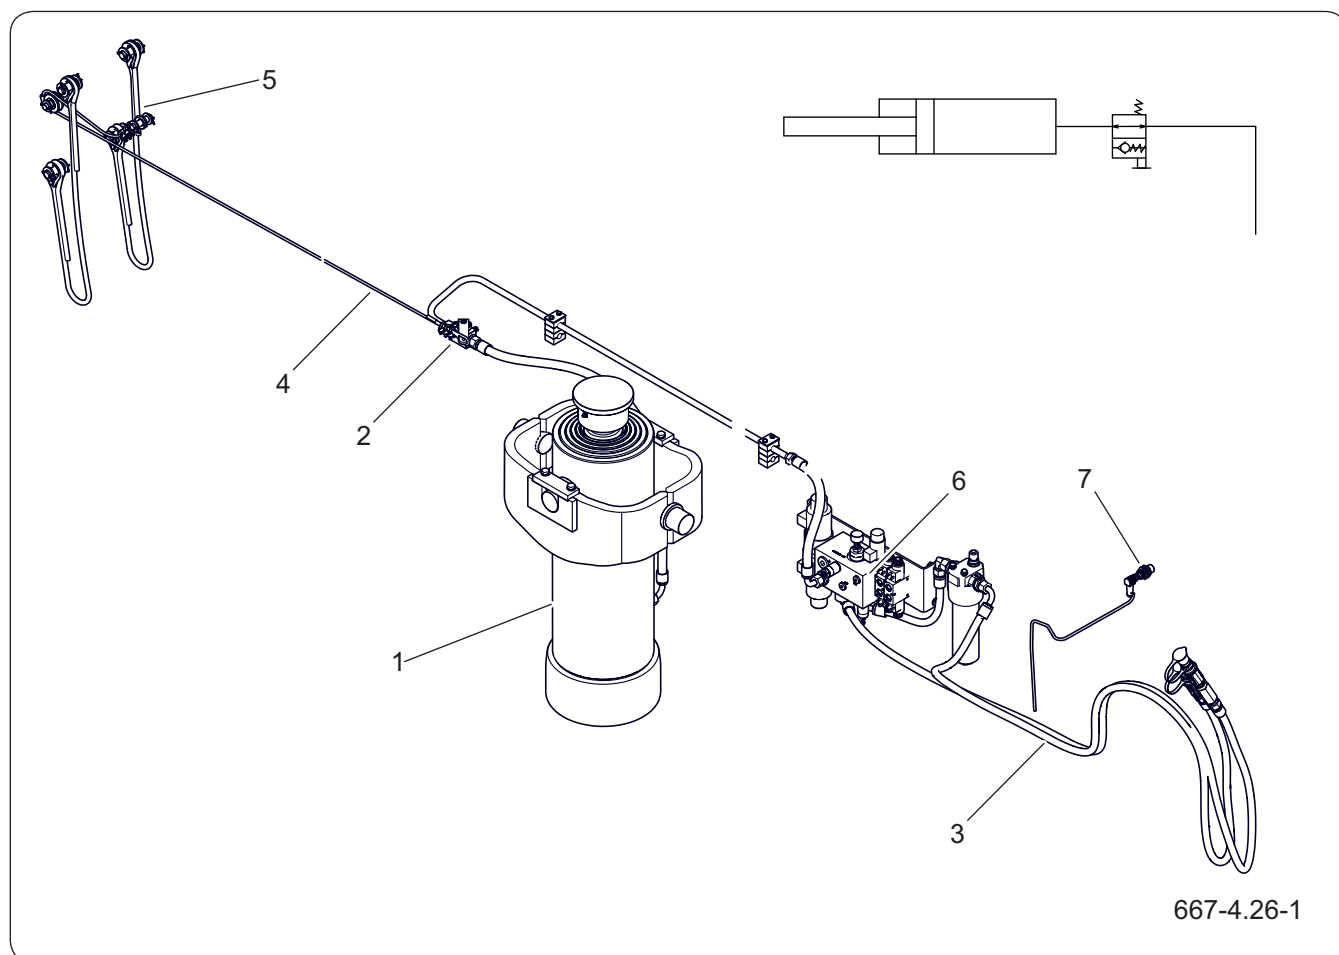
Konstrukce a schéma hydraulické instalace vyklápění pro mechanické zavěšení s bloádou zavěšení
